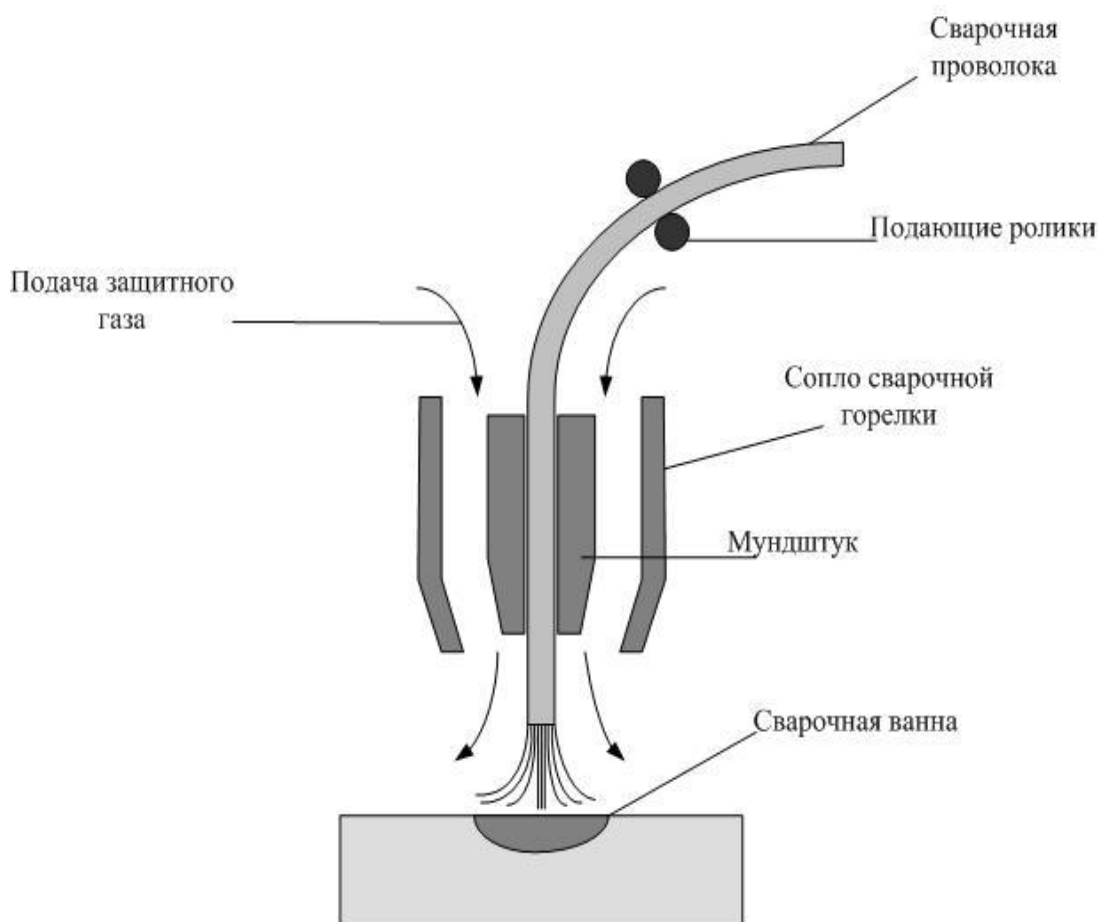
Схема подвода защитного газа, сварочной проволоки и сварочного тока к плавящемуся электроду (сменный мундштук).
